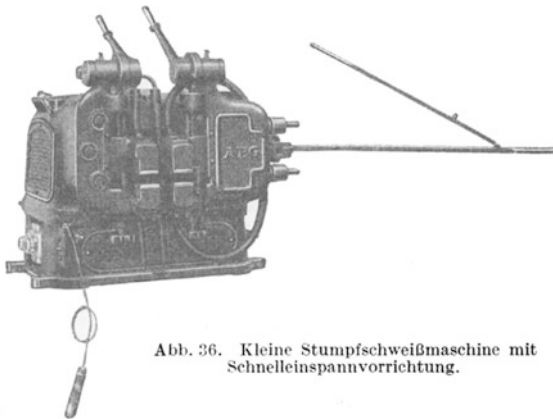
Kleine Stumpfschweißmaschine mit Schnelleinspannvorrichtung.
